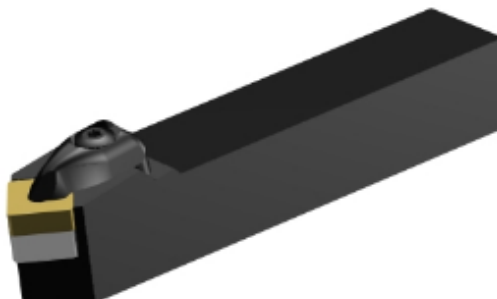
Маркування корпусу різця для напівчистої обробки DCLNR 2020K 12
